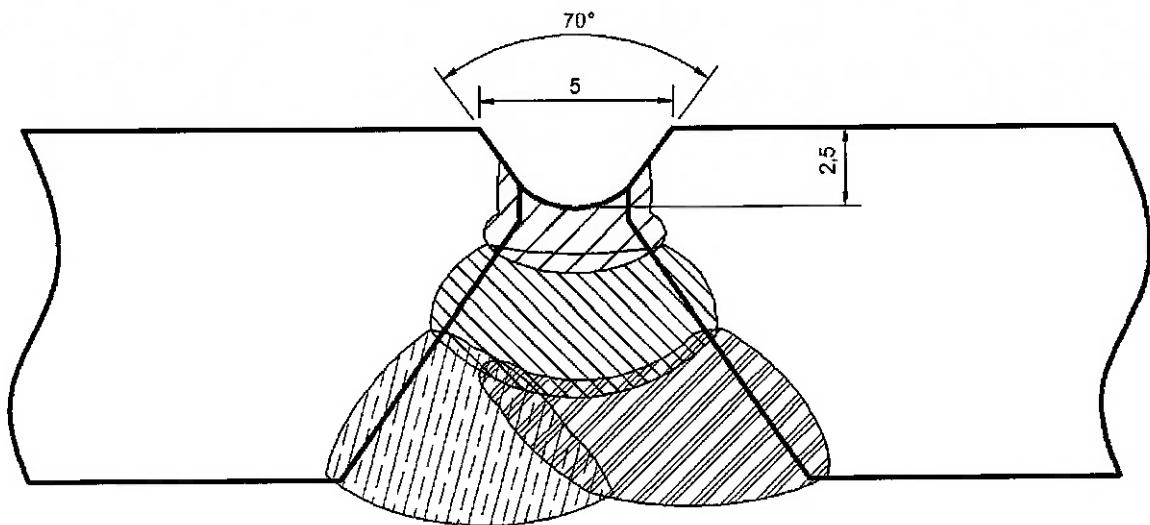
Goivagem da raiz da junta soldada.
